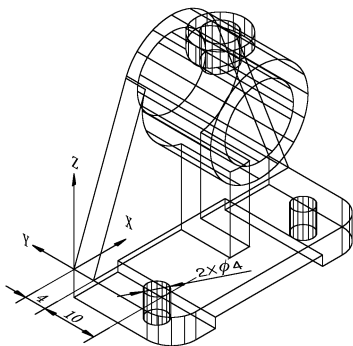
标注轴承座底板上底面、支撑板、肋板部分尺寸
